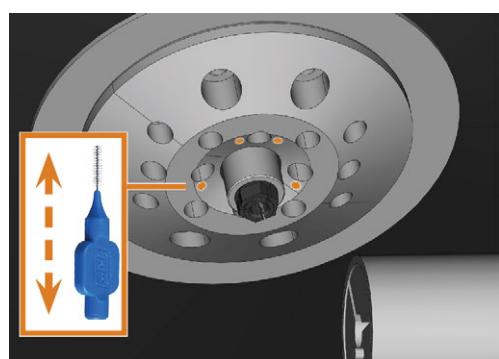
LIMPIEZA DE LA PLACA DE BOQUILLAS; BOQUILLAS MARCADAS EN NARANJA (EL NÚMERO DE BOQUILLAS DE SU MÁQUINA PODRÍA SER DIFERENTE)
